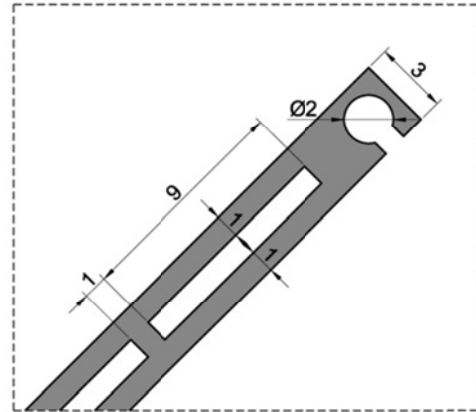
Alzado y planta del panel. Fuente: (Elaboración propia).
